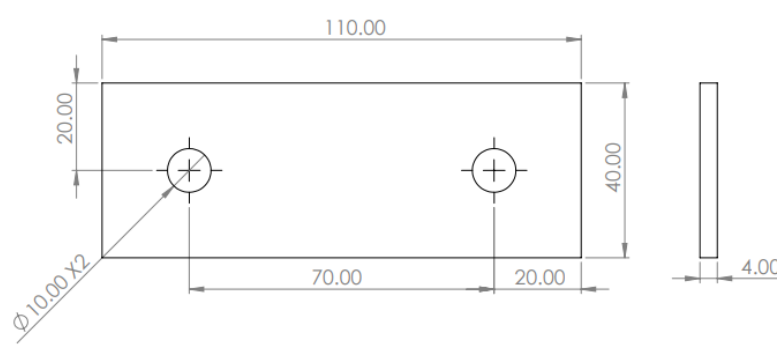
Dimensiones del martillo. (Cotas en mm). Fuente propia.
